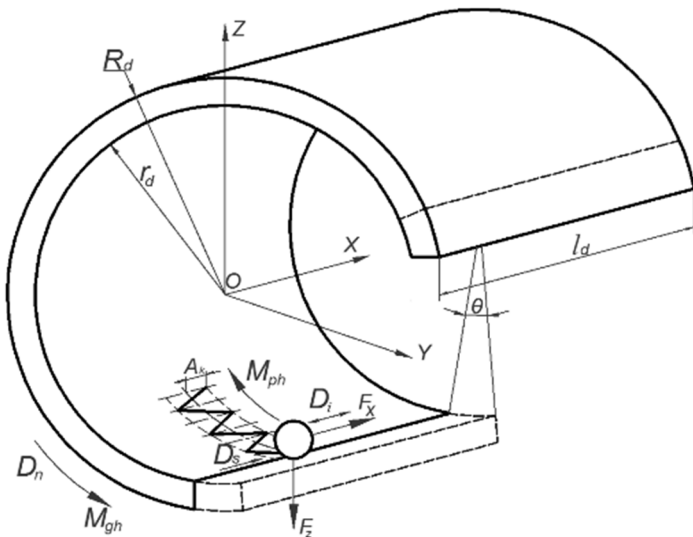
Схема переносного обертального руху заготовки при формуванні регулярного мікрорельєфу на внутрішній циліндричній поверхні
